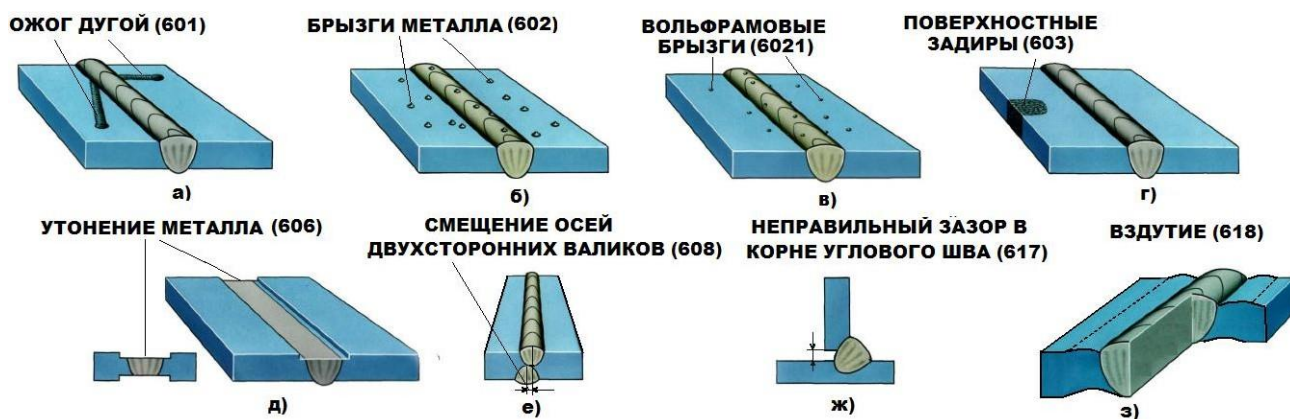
Классификация отклонений формы и размера сварного шва по ГОСТ Р ИСО 6520-1-2012: а – ожог дугой; б – брызги металла; в – вольфрамовые брызги; г – поверхностные задиры; д – утонение металла; е – смещение осей двухсторонних валиков; ж – неправильный зазор в корне угловых швов; з – вздутие
